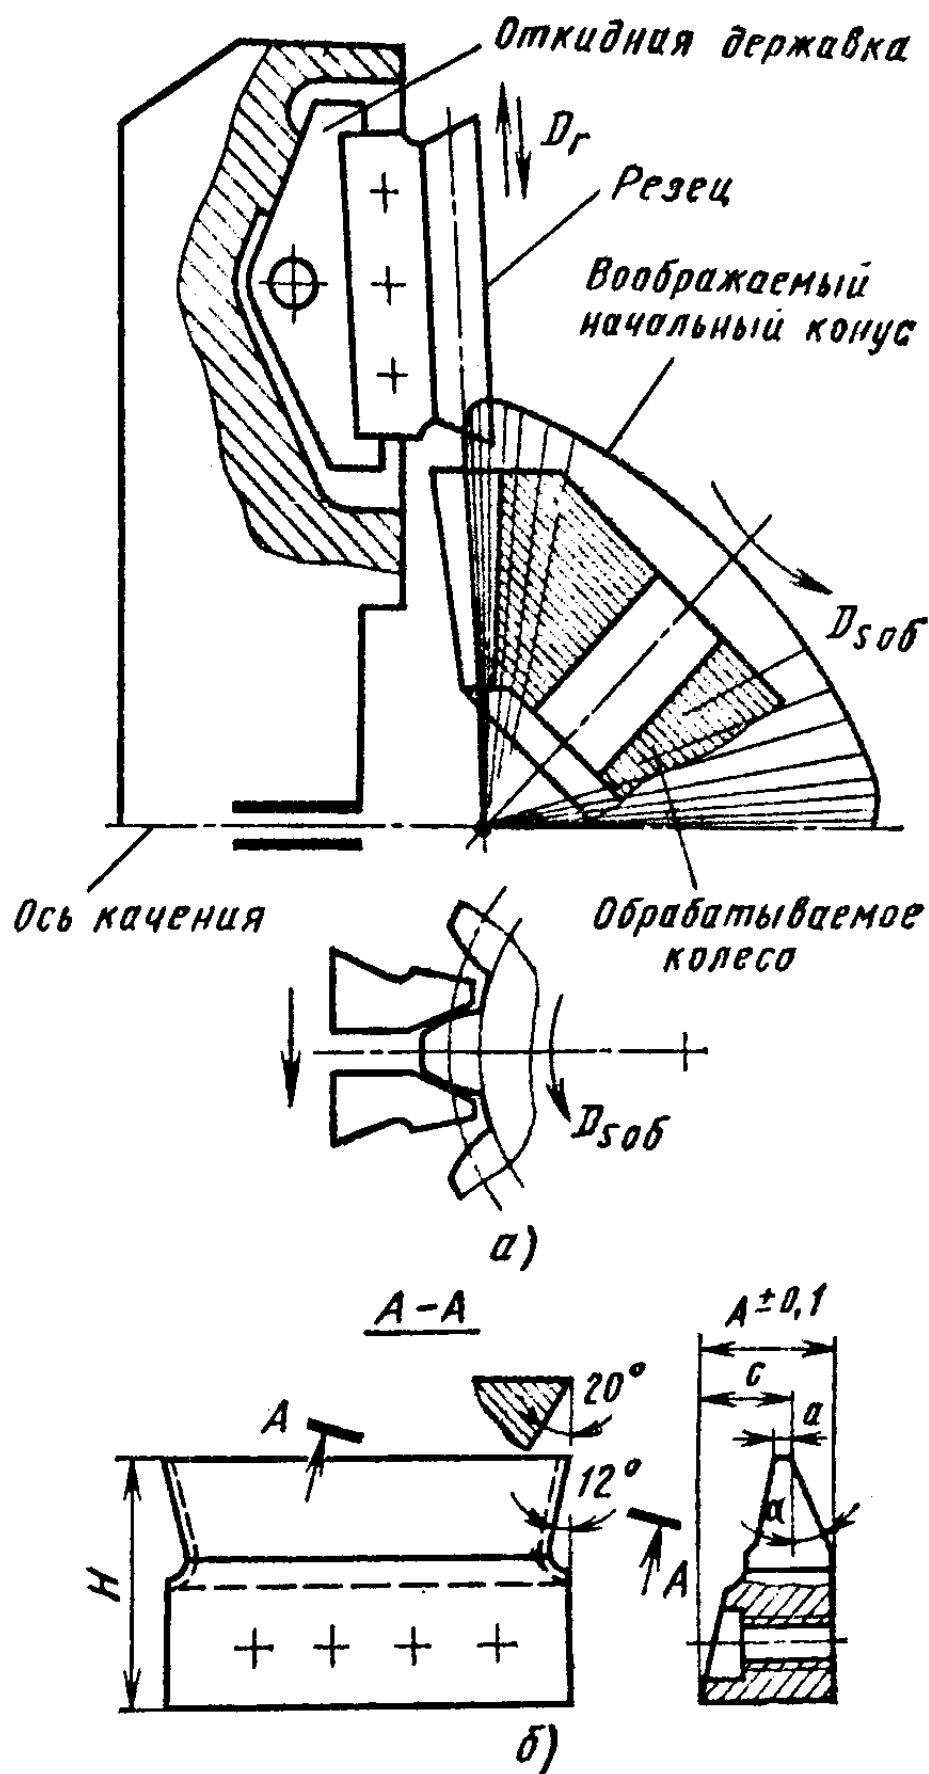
Схемы зубо-строгания конических колес (а) и конструкция строгального резца (б)
